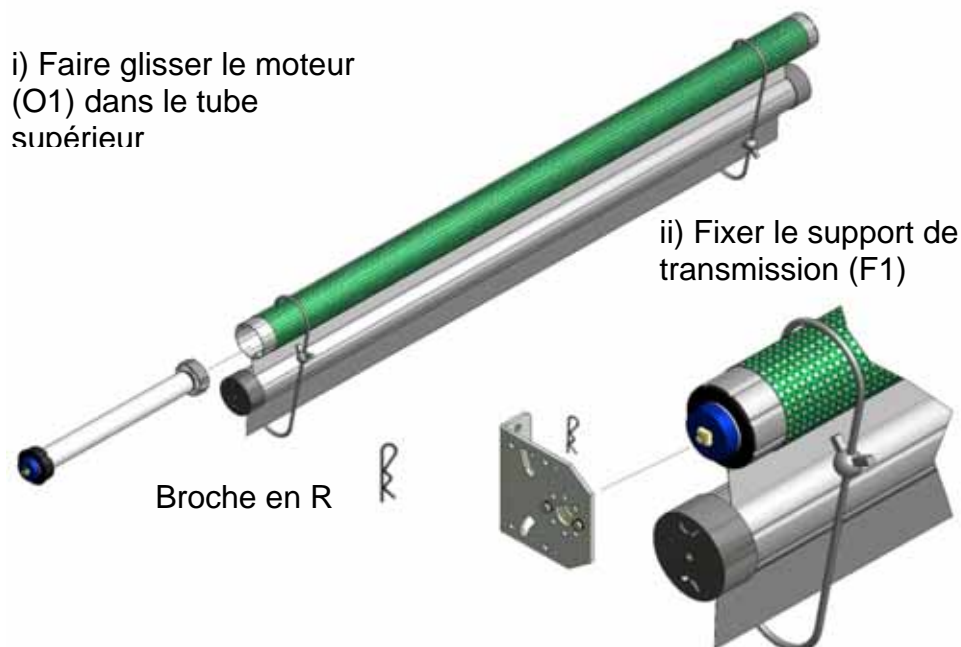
, Moteur inséré dans le tube supérieur et support de transmission fixé
